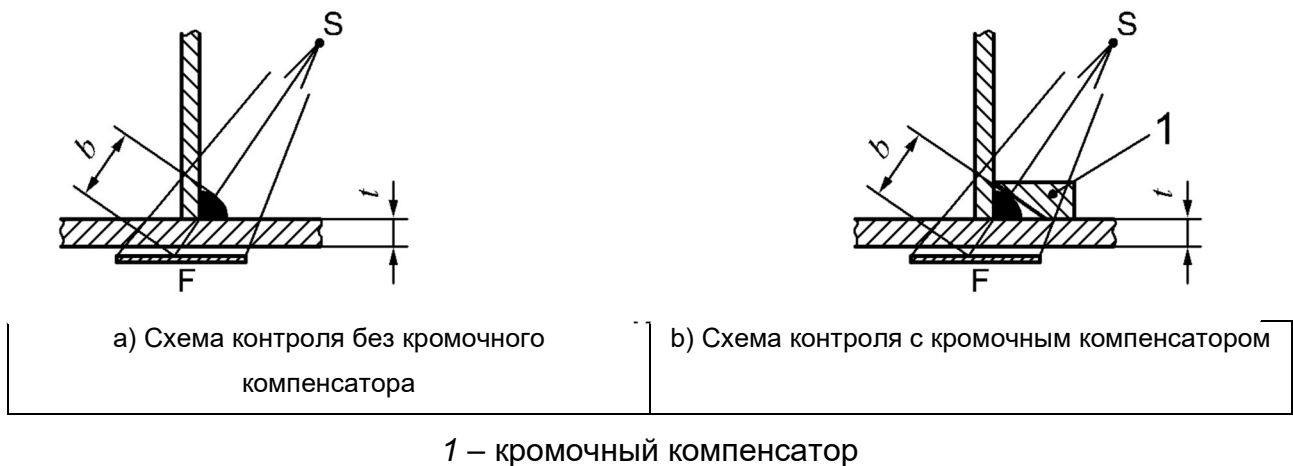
Схема контроля при просвечивании угловых сварных швов с наклонным положением пленки
